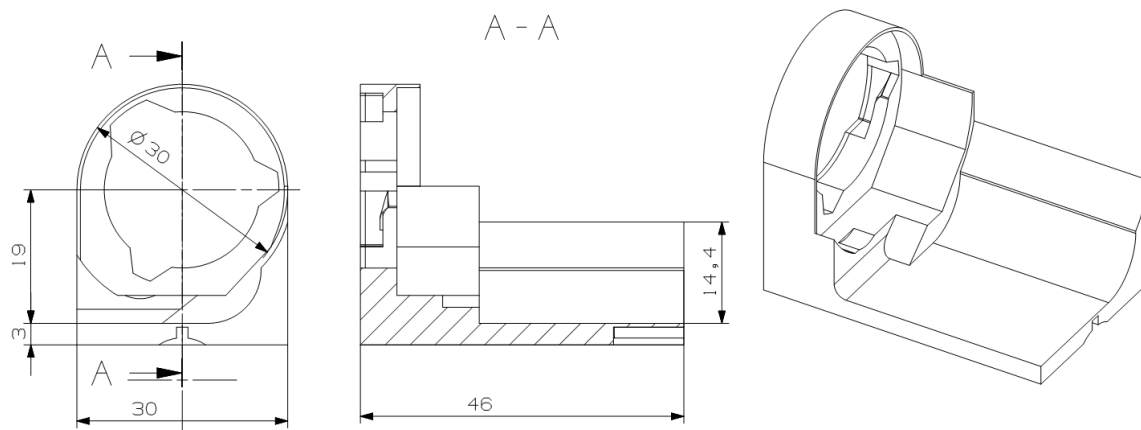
Montáž motorku do konzoly (max. zástavbový prostor) v horizontální poloze (90°)
